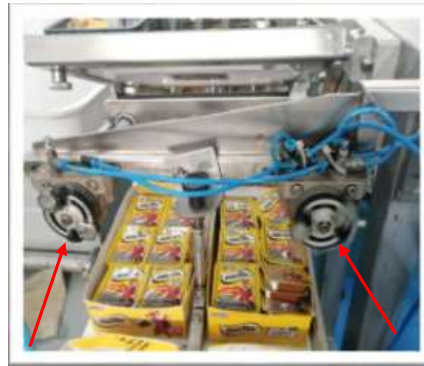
dispositivo de alimentación por gravedad instalado en el equipo
